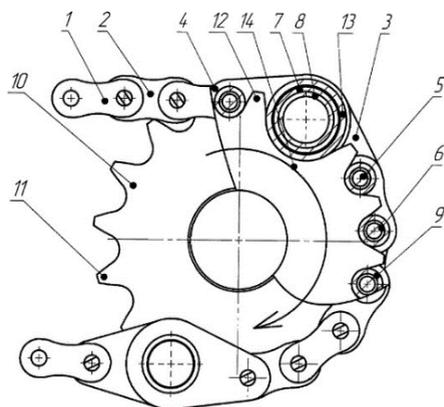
Устройство цепной передачи с увеличенным ресурсом:
